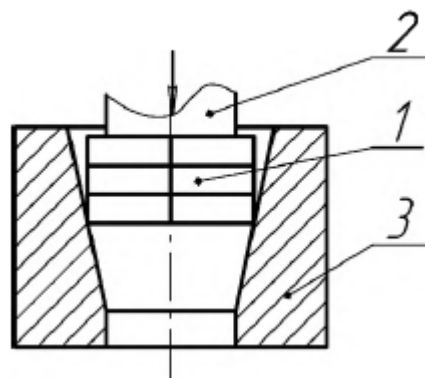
Переформування заготовок продавлюванням через матрицю 1 - пакет заготовок; 2 - пуансон; 3 - матриця
